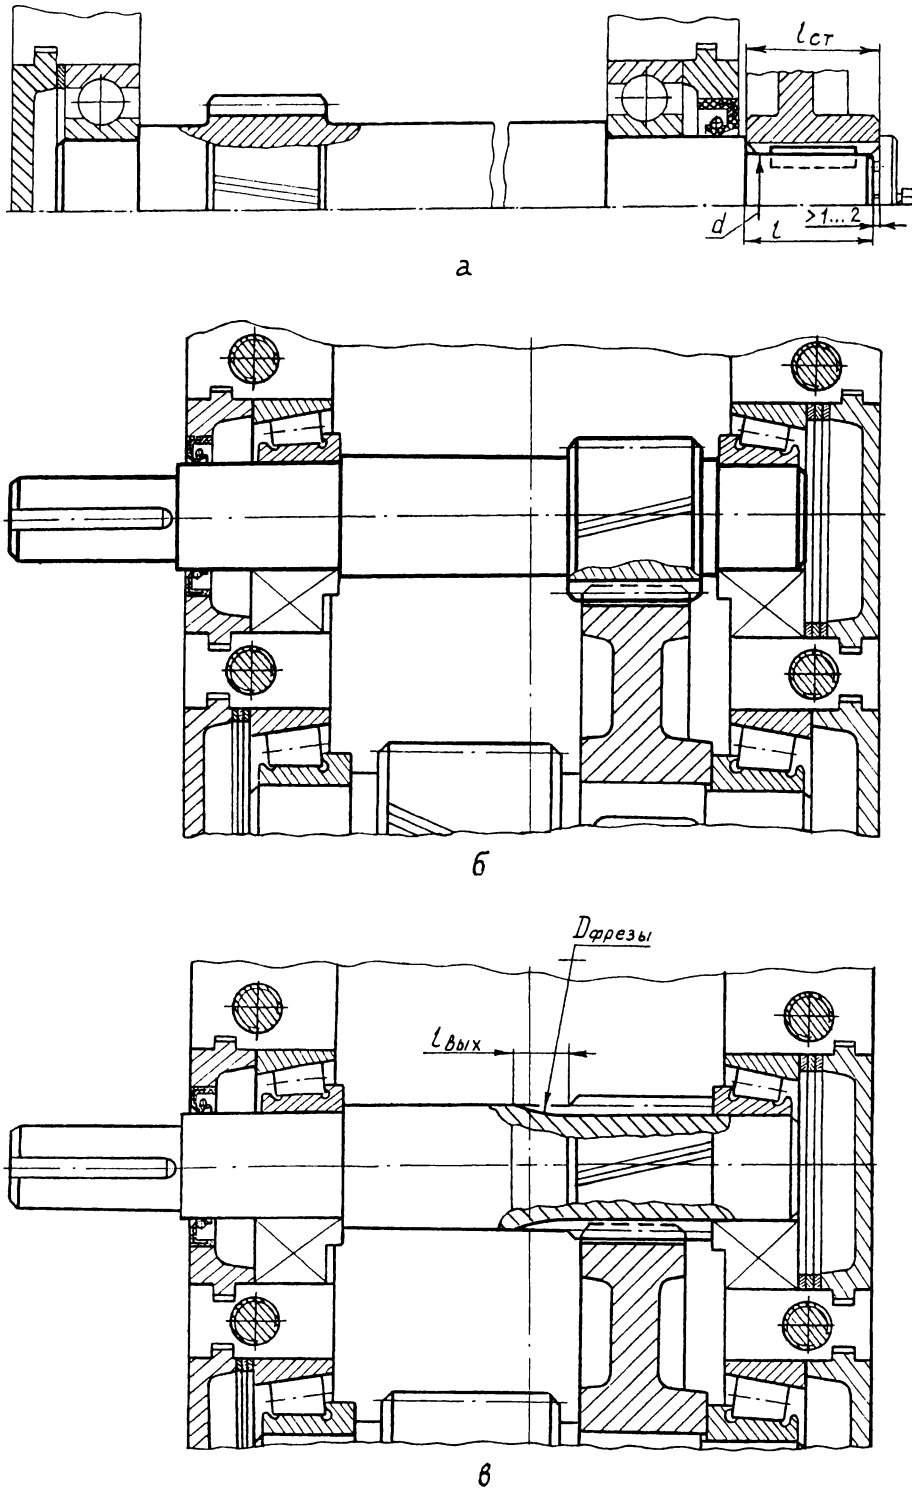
Вал-шестерня цилиндрического двухступенчатого зубчатого редуктора, выполненного по развернутой схеме:
